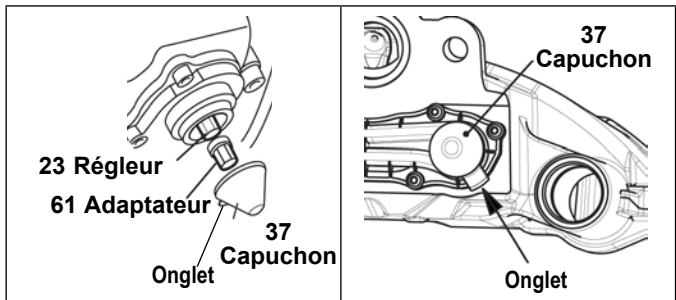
VUE EXPLOSÉE DU RÉGLEUR ET DE L'ADAPTATEUR
